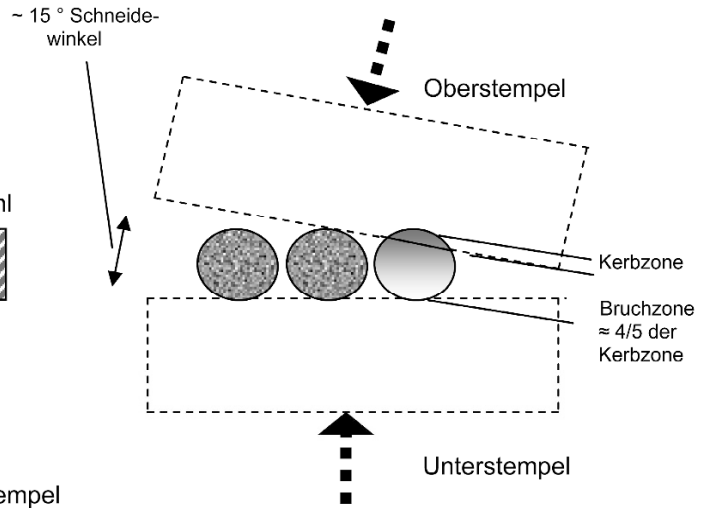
Struktur der Schnittfläche längs zum Betonstahlstab betrachtet
